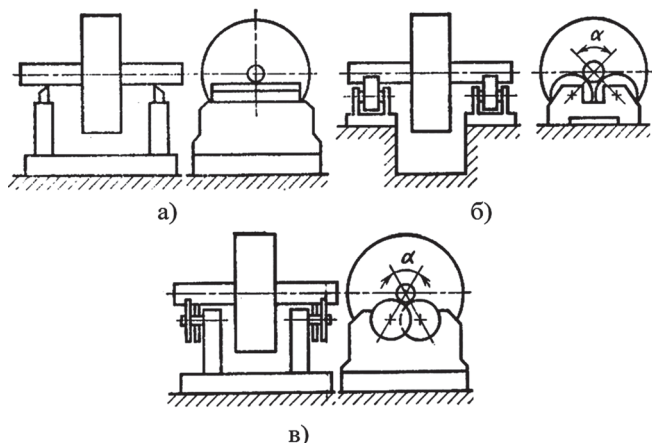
Схемы установок для статической балансировки вращающихся деталей и сборочных единиц:
